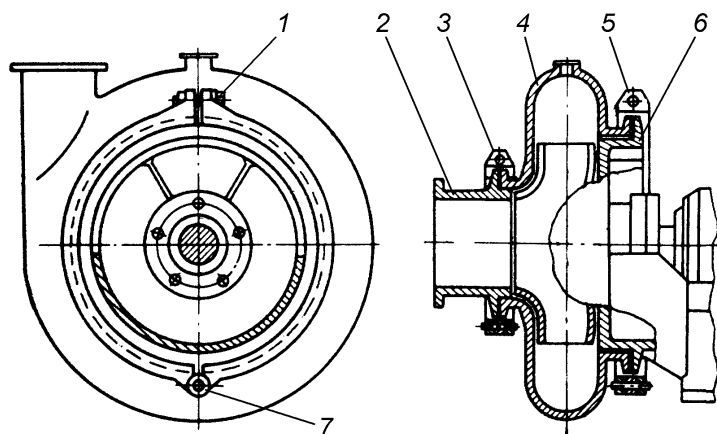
Корпус ґрунтового насосу, що кріпиться за допомогою швидкокороз’ємних з’єднань: 1 – стяжний болт; 2 – всмоктувальний патрубок; 3, 5 – шарнірні кільця; 4 – корпус; 6 – задня кришка; 7 – шарнір
